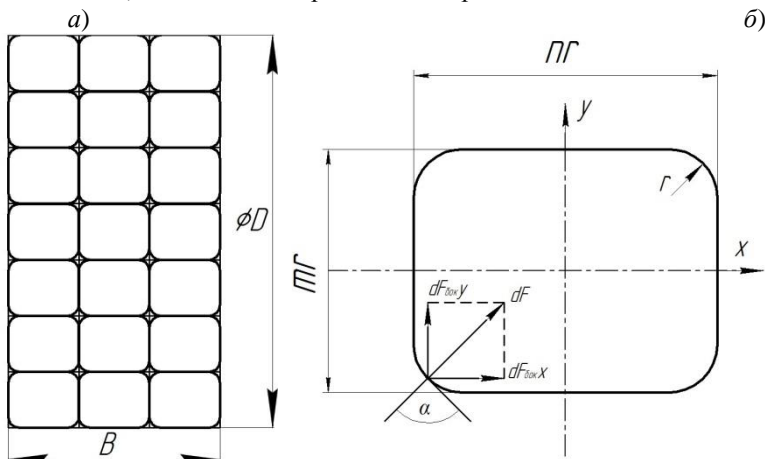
Рабочая поверхность бандажа валка с наплавленной футерующей сеткой:
